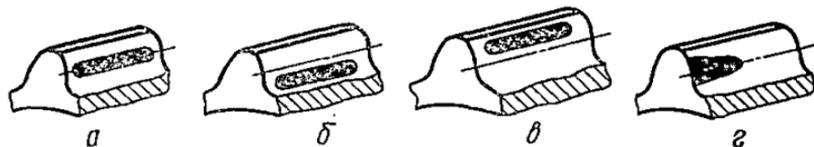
Расположения пятна контакта на зубе колеса цилиндрической передачи при межцентровом расстоянии:
